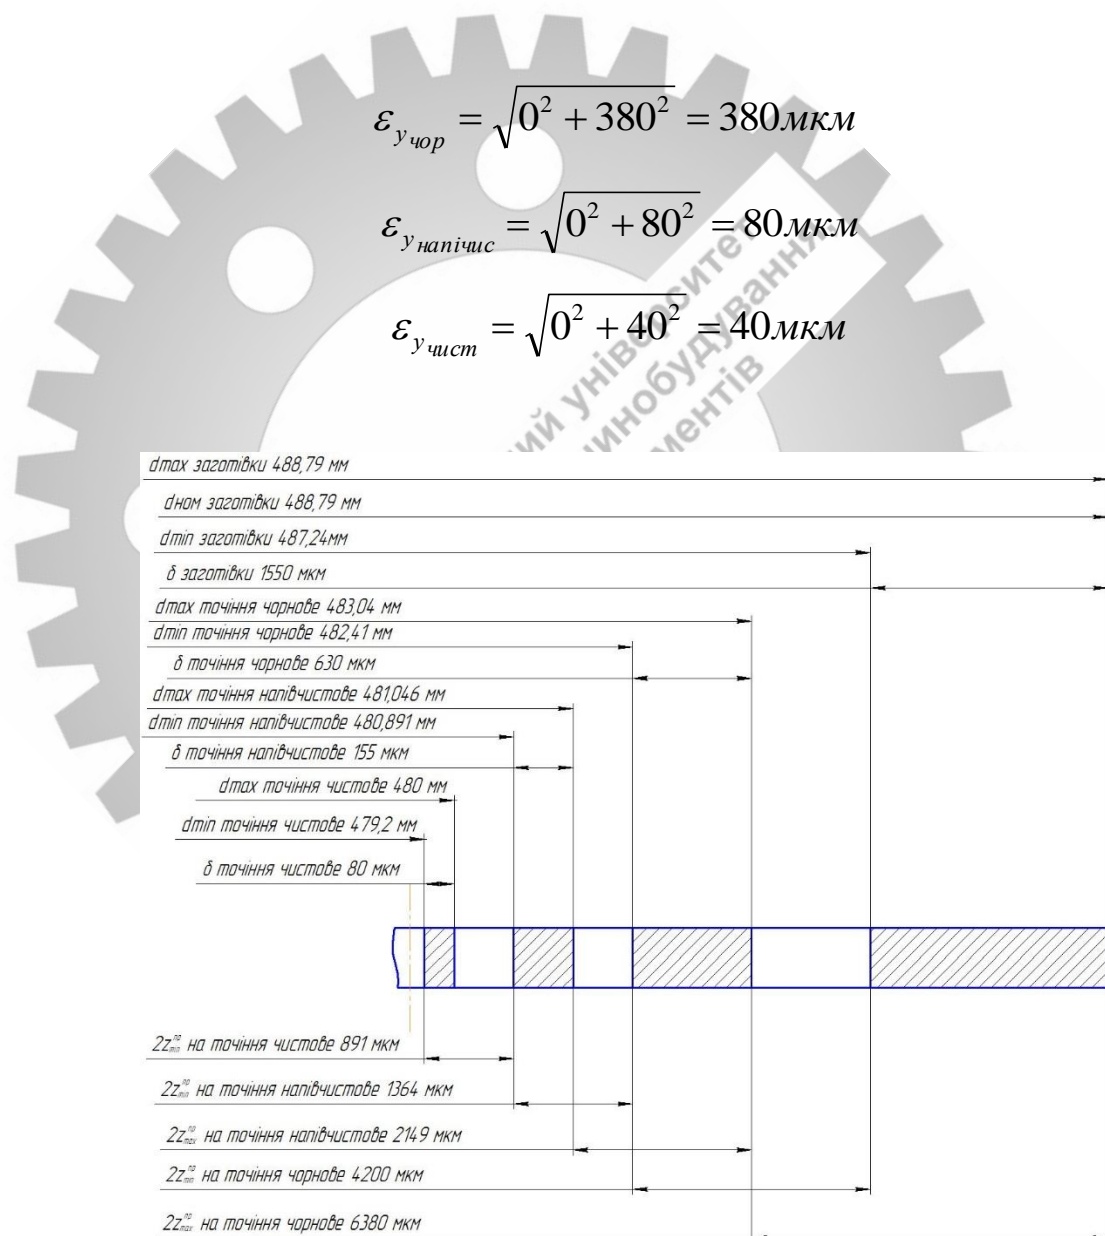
Схема графічного розташування припусків і допусків на обробку зовнішньої поверхні $\varnothing 480 \text{ h}7 \left(\begin{smallmatrix} 0 \\ -0,8 \end{smallmatrix} \right)$.
